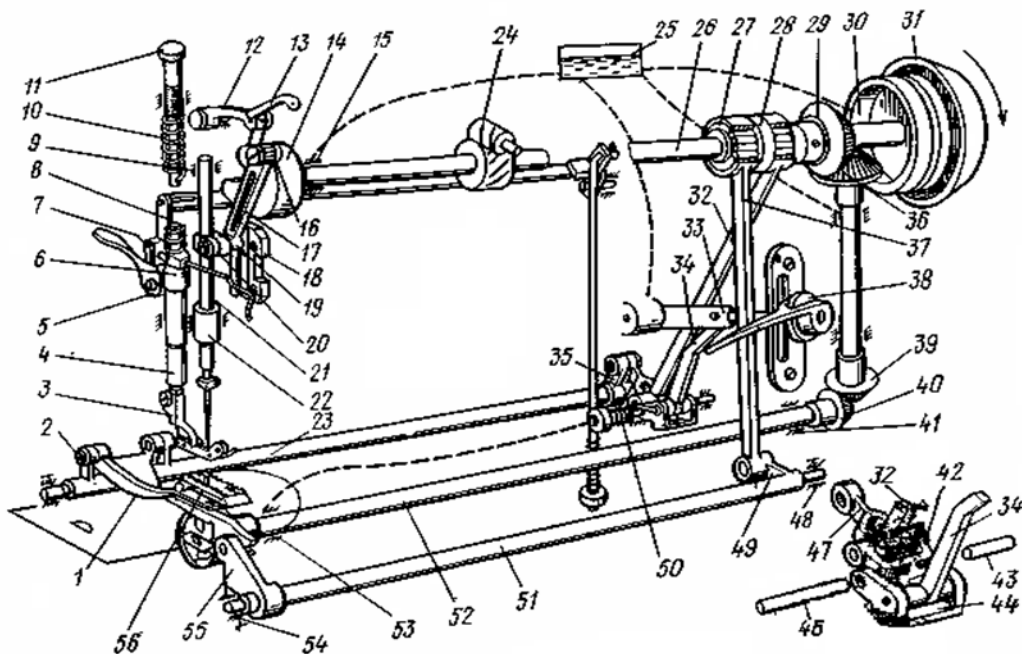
Схема конструкции швейной машины 1022 кл.
